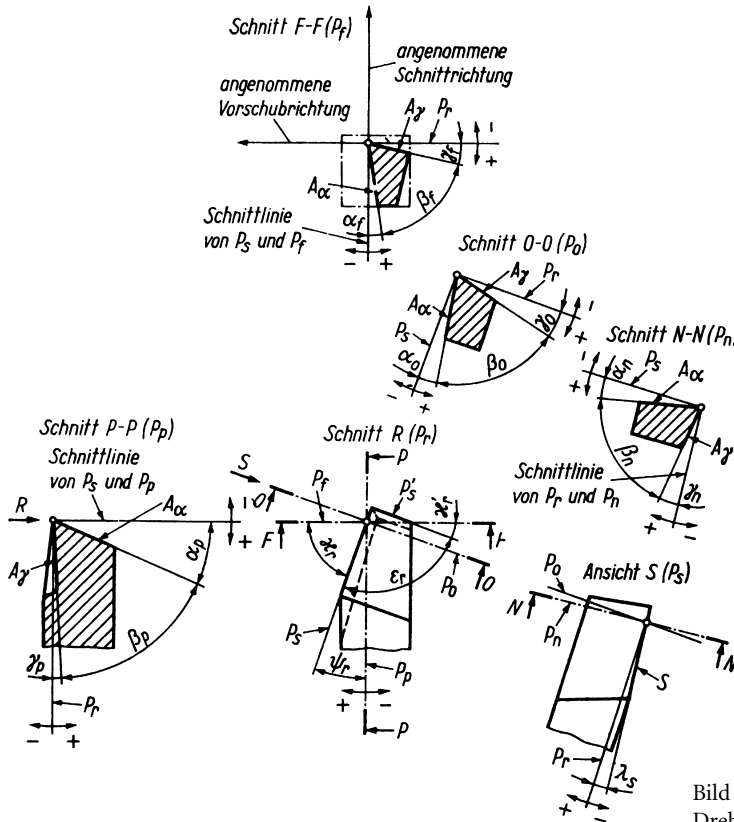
Werkzeugwinkel am Drehmeißel (nach DIN 6581)
